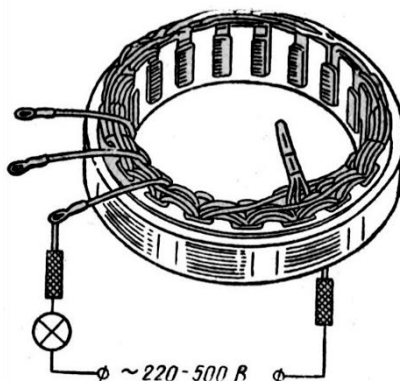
Перевірка обмотки статора на замикання з корпусом
